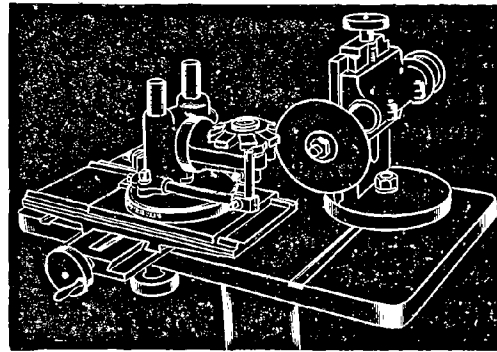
Disposition pour fraise à tailler les engrenages.
